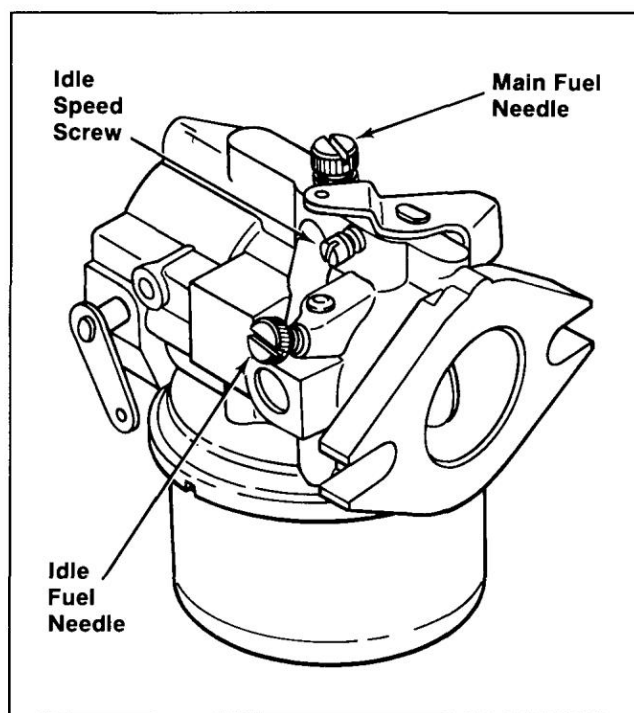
Carburateur à jet réglable construit par Kohler.
